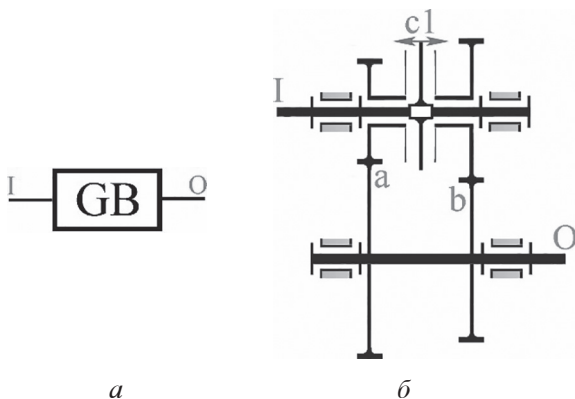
Обобщенная (а) схема и кинематическая (б) схема двухступенчатой коробки передач с неподвижными осями зубчатых колес:
